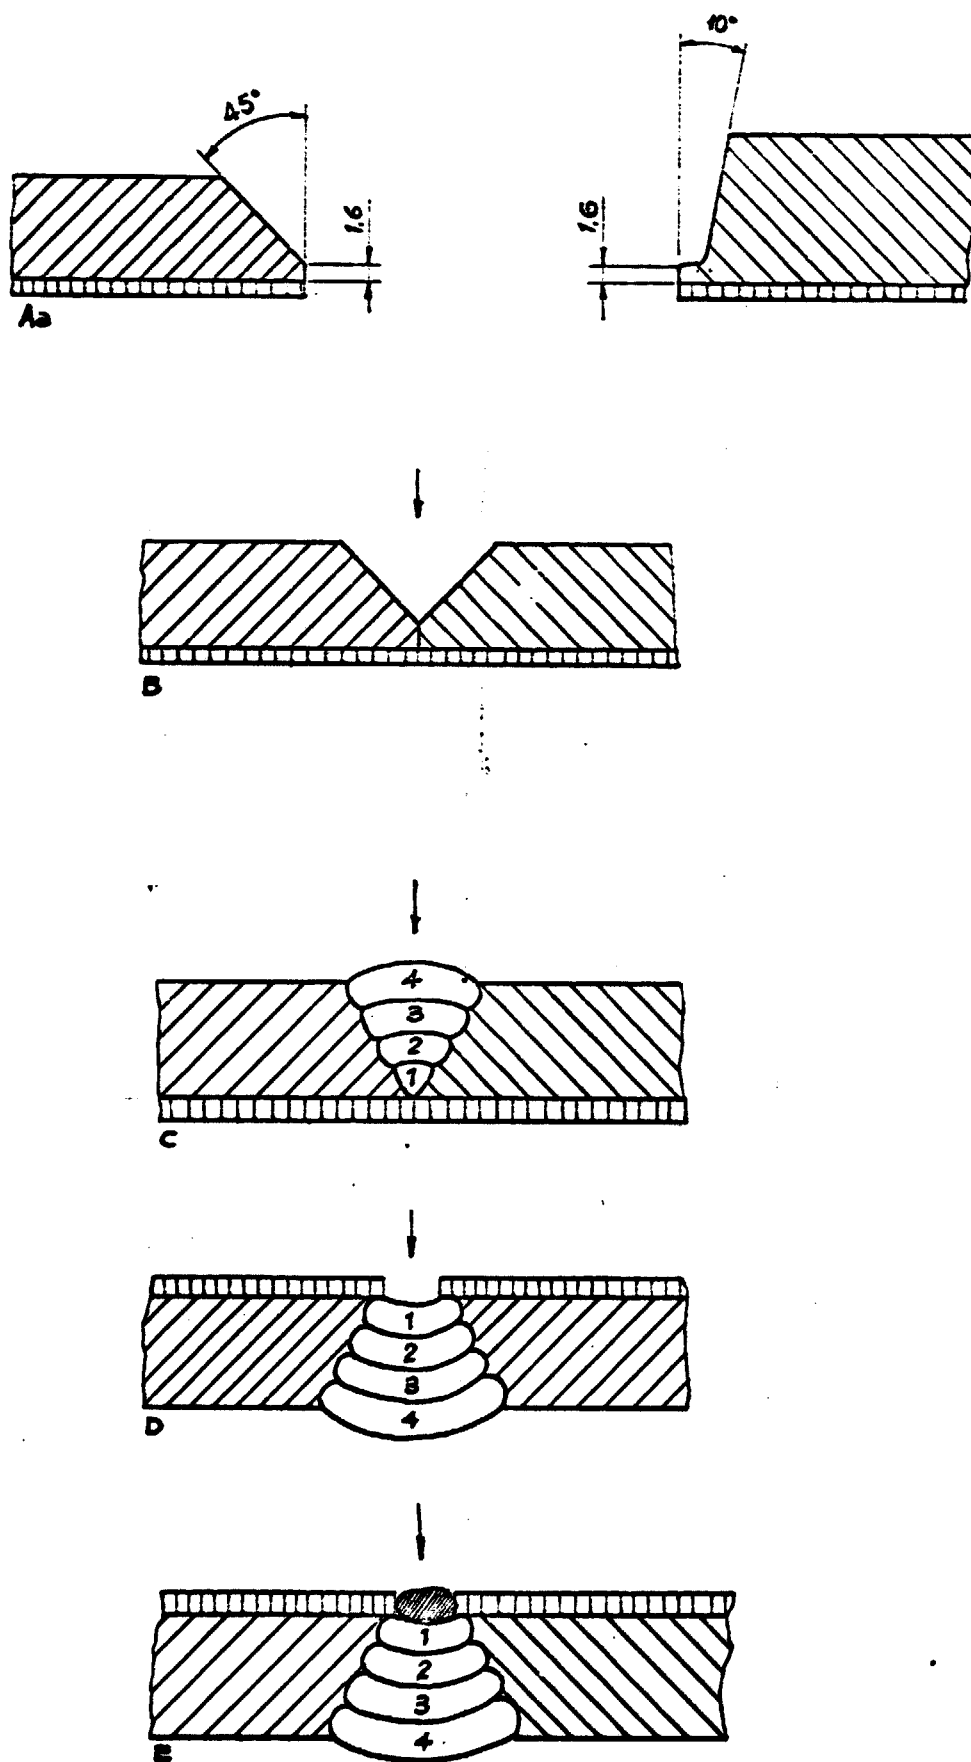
SOLDADURA A TOPE DE ACERO PLAQUEADO.
